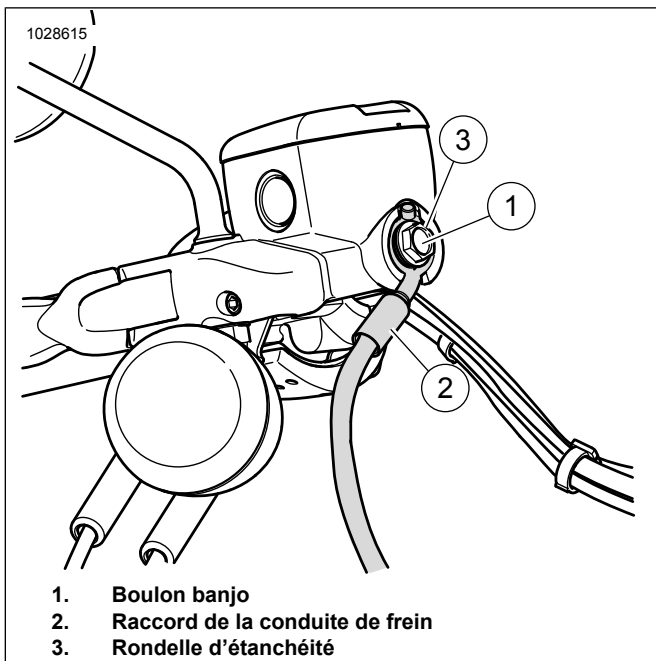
Raccord de conduite de frein, boulon banjo et joint
